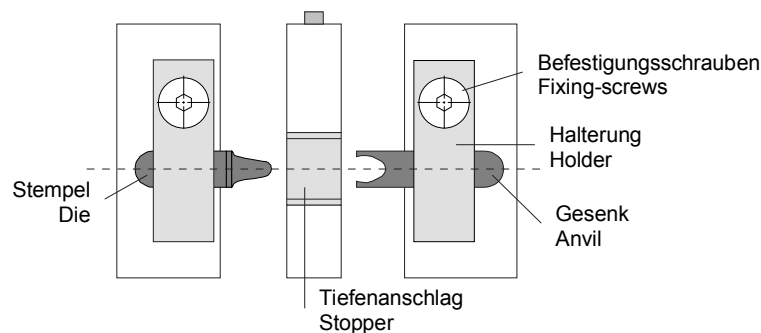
Crimpwerkzeug / Crimping tool
